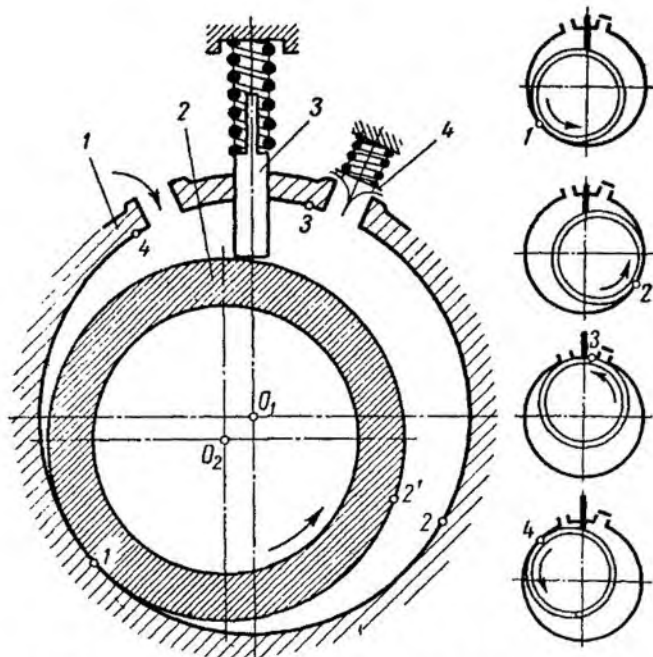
Схематичный разрез ротационного компрессора с катящимся ротором:
